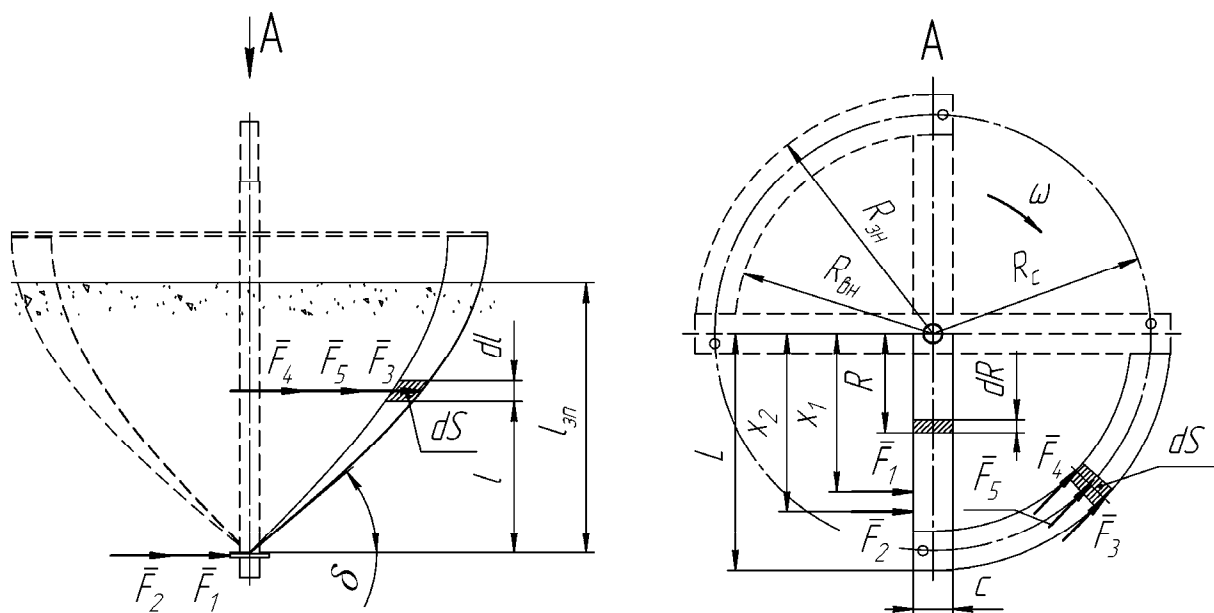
Схема сил, що діють на робочий орган змішувача
